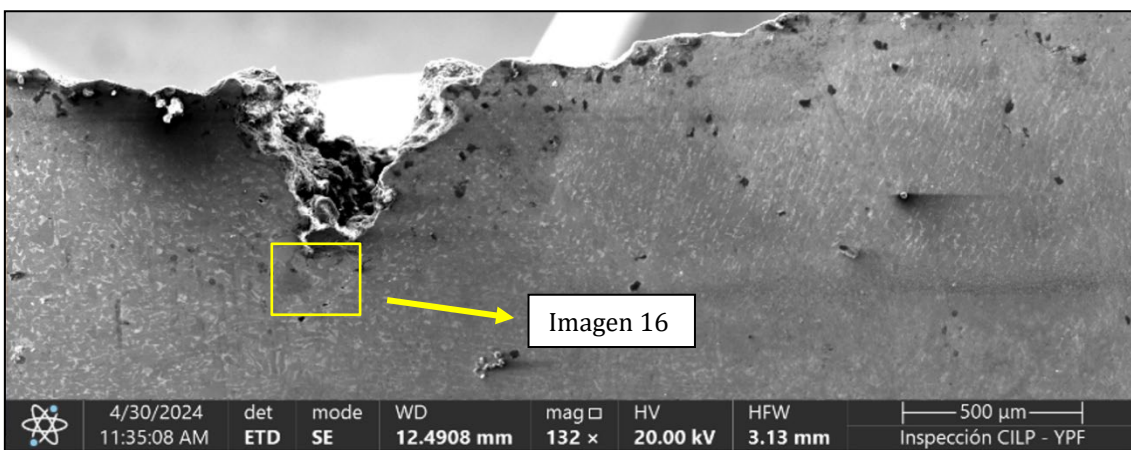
Codo inferior. Soldadura longitudinal con corrosión localizada en la ZAC.
